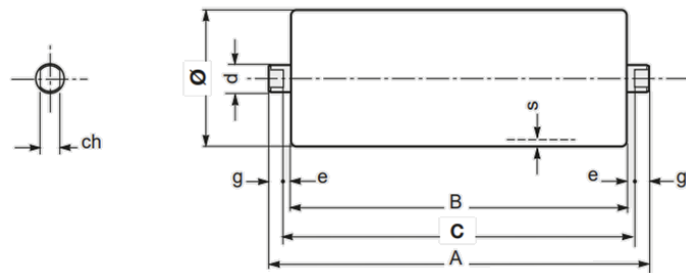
Pražec dvouválečkový Interroll 314 T [22]
